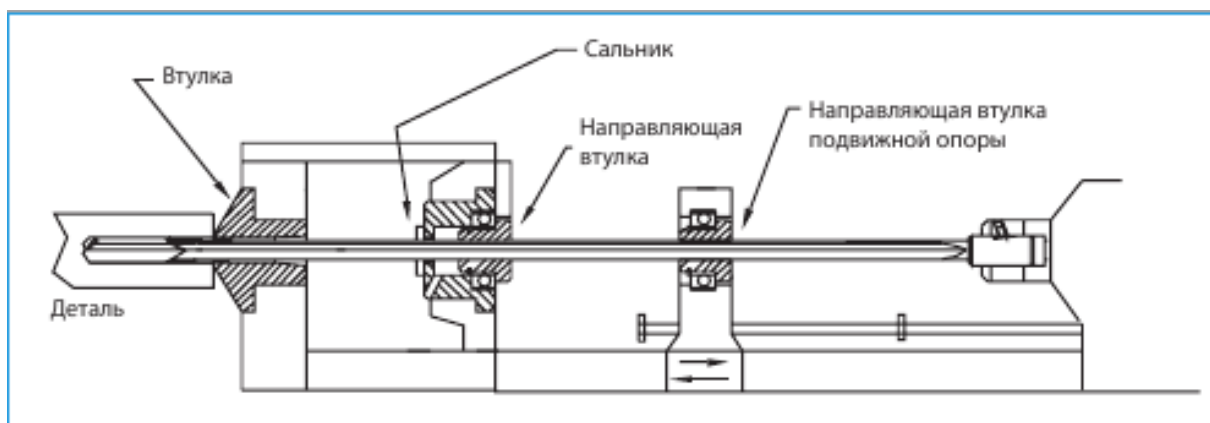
Принадлежности для сверления ружейными сверлами
